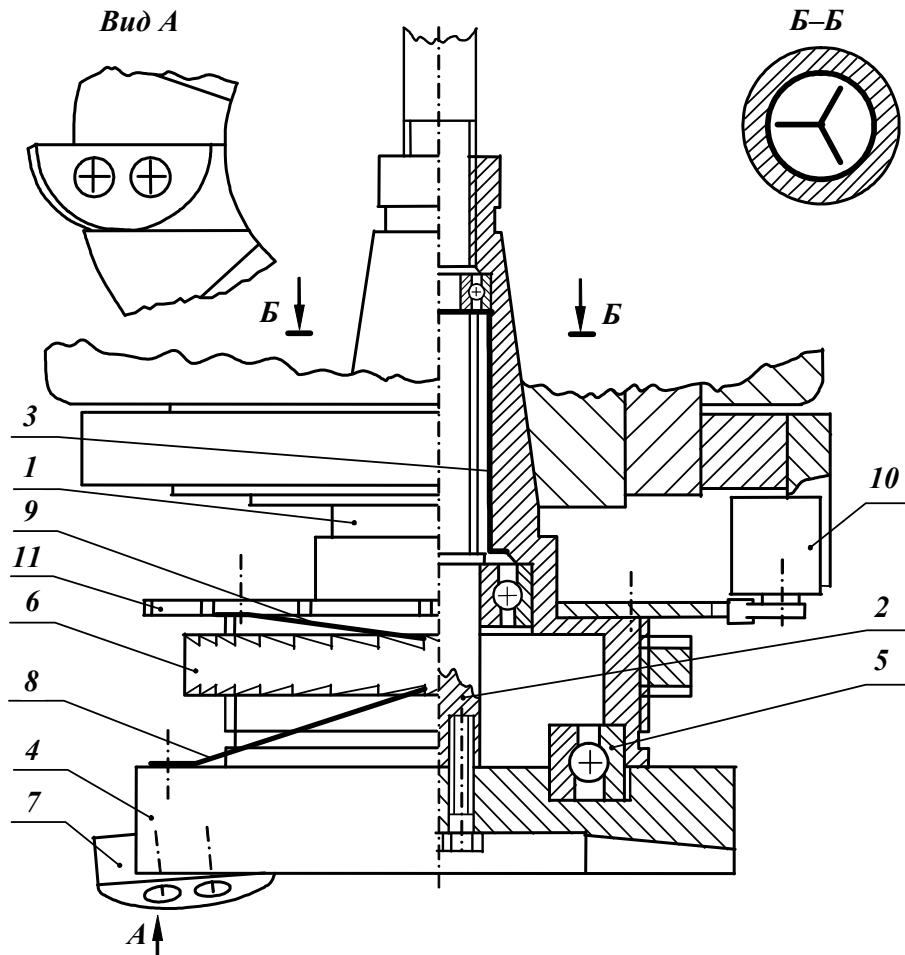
Схема конструкції механічного фрезерного динамометра
